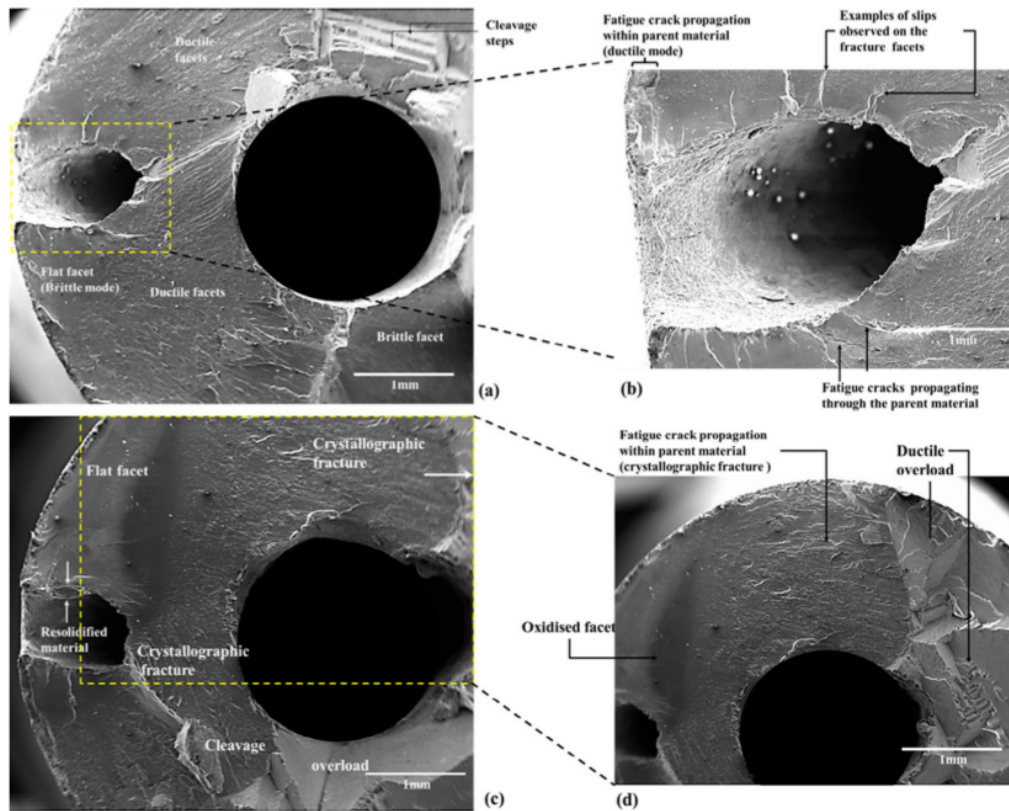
Fractographie d’une rupture auprès d’un Shaped Hole après un essai de fatigue LCF à gradient thermique [18].
